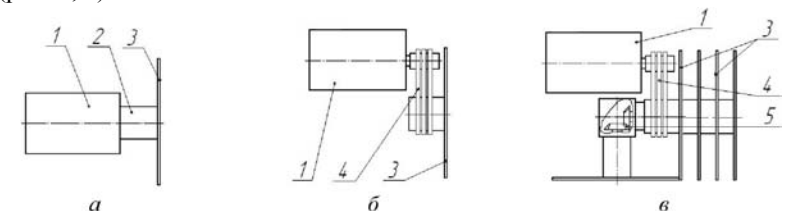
Принципові схеми механізмів різання з різними способами передачі обертового руху: а – безпосередньо валом двигуна; б – клиноповою передачею; в – клиноповою передачею та конічним редуктором; 1 – двигун; 2 – вал двигуна; 3 – кругла пилка; 4 – клинопосова передача; 5 – конічний редуктор
